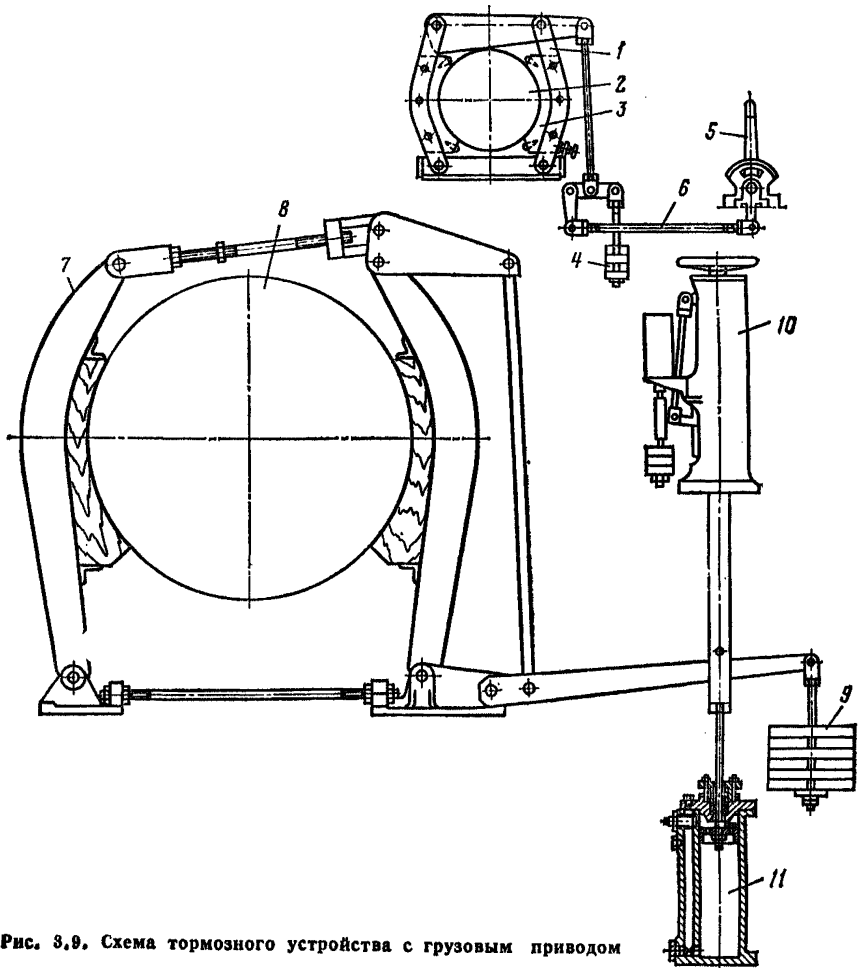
Схема тормозного устройства с грузовым приводом
